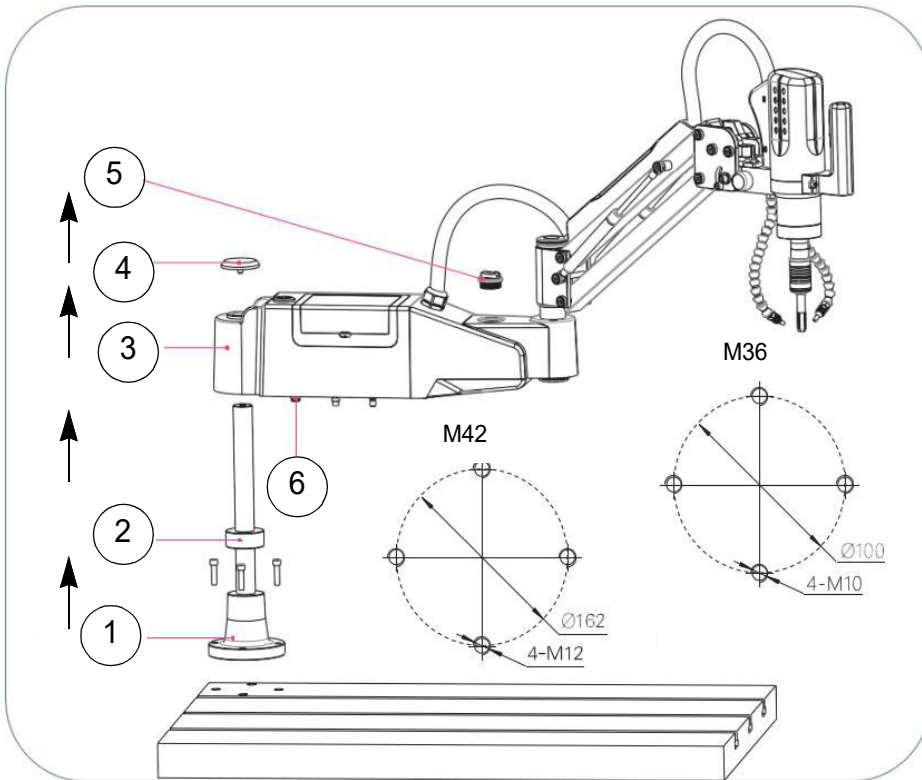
Befestigungslöcher für den Maschinenträger
